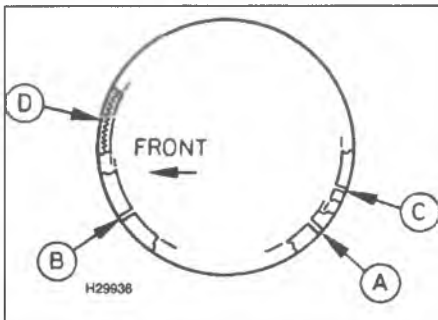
Расположение замков поршневых колец – бензиновый двигатель
